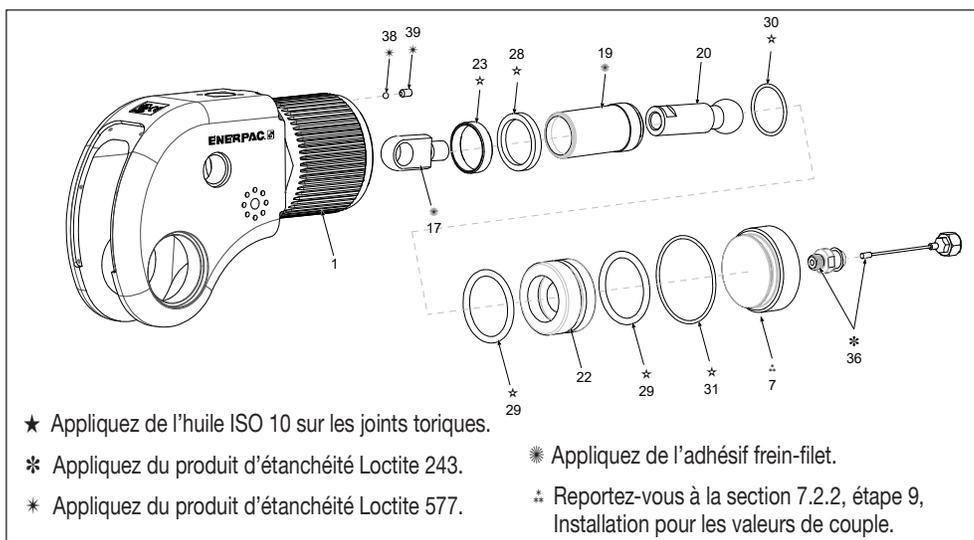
Vue éclatée des pistons DSX11000 et DSX25000
